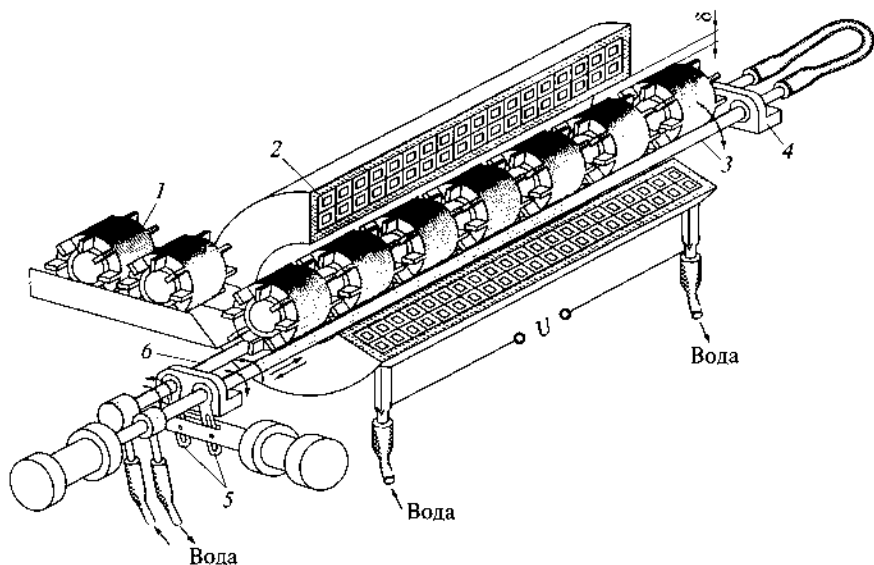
Индукционный нагреватель с поштучной выдачей деталей: 1 — собираемые роторы; 2 — индуктор; 3, 6 — направляющие штанги; 4 — держатель штанг; 5 — устройство поворота штанг
